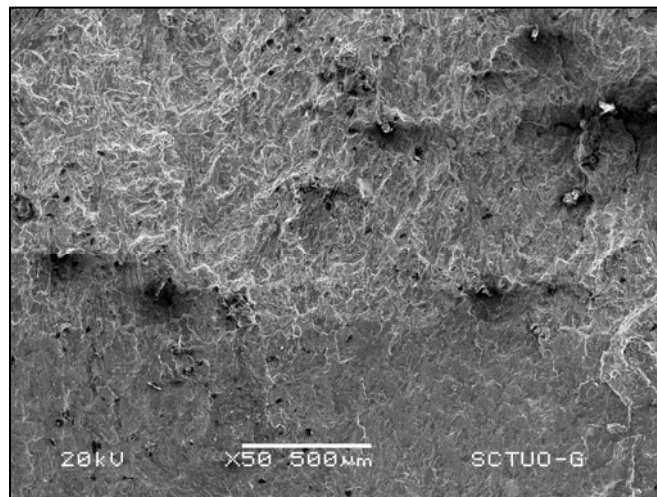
Aspecto general de la superficie fracturada creada justo a continuación de la grieta generada por fatiga en el ensayo de tenacidad a fractura de la fundición alta en cromo (50x)
